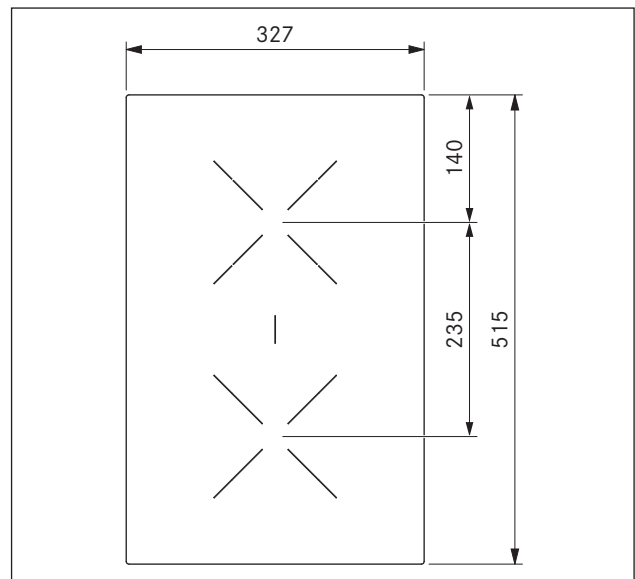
CKCB apparatets dimensjoner sett ovenfra
